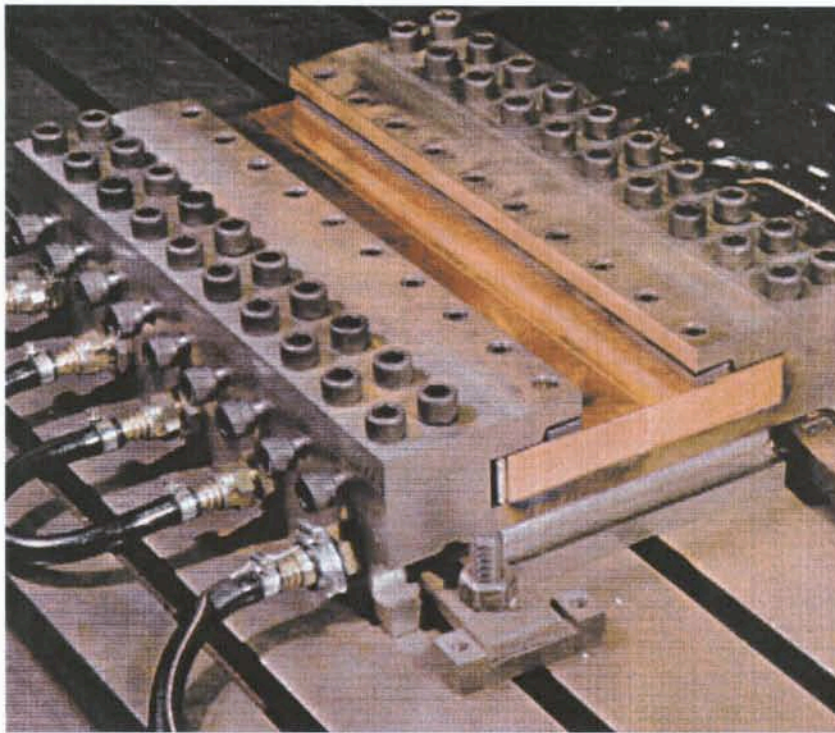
Sammanfogning med friction stir welding.
